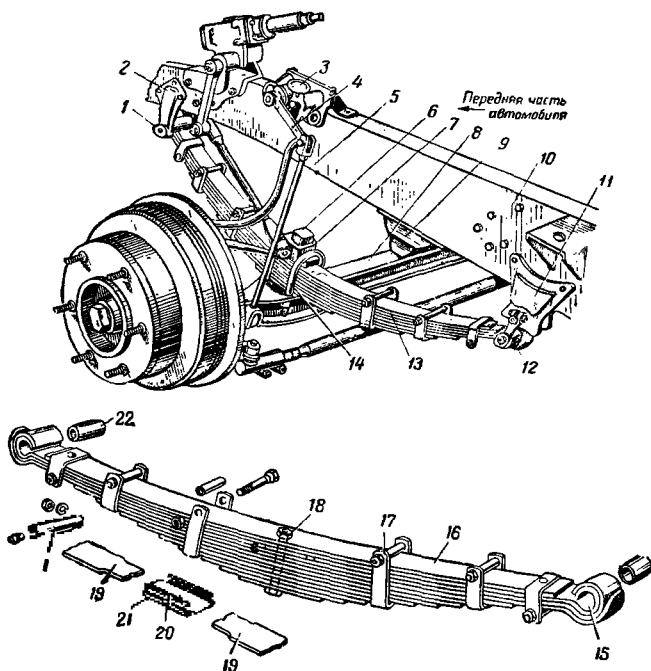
Соединение передней рессоры с осью и рамой автомобиля ГАЗ-51 (вверху) и детали полуэллиптической рессоры (внизу).
